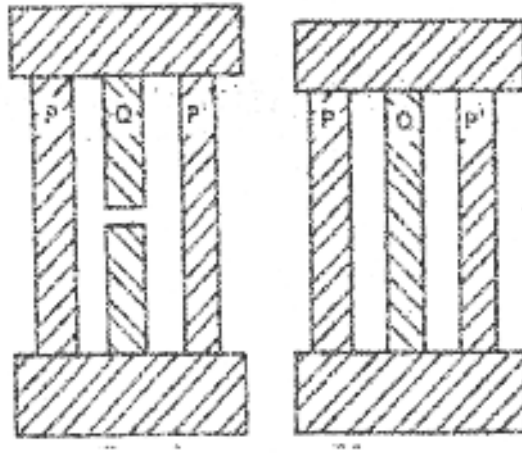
Kaynaklı bir parçada kalıntı gerilmeler [2]
